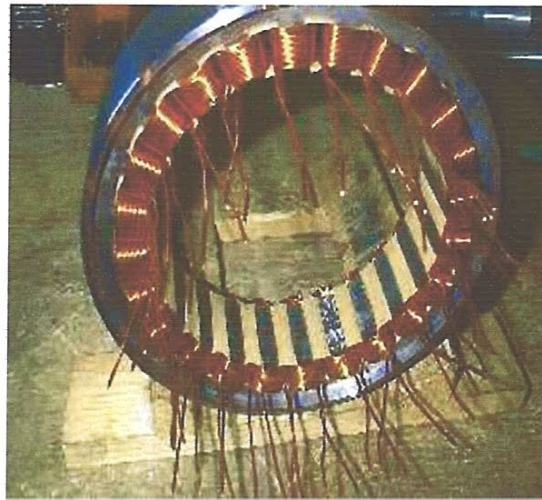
Bobinage concentré pour machine à flux radial [1]
